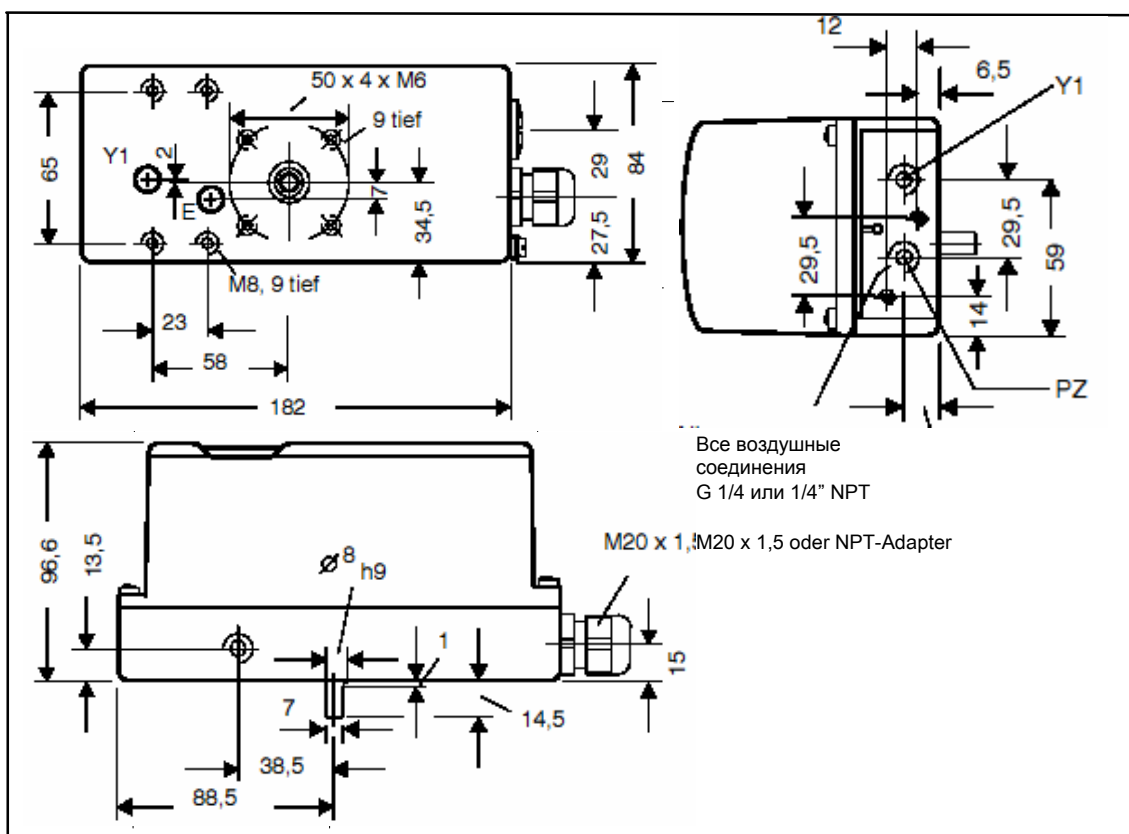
Габаритный чертеж конструкции в металлическом корпусе 6DR5xx1
